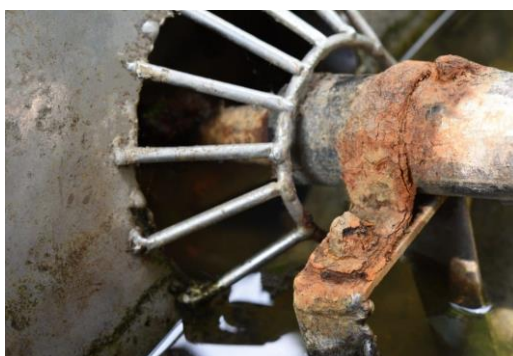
Руйнування деталей, яке потребує зварювання
